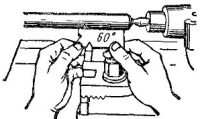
Установка резьбового резца по шаблону при нарезании наружной резьбы
